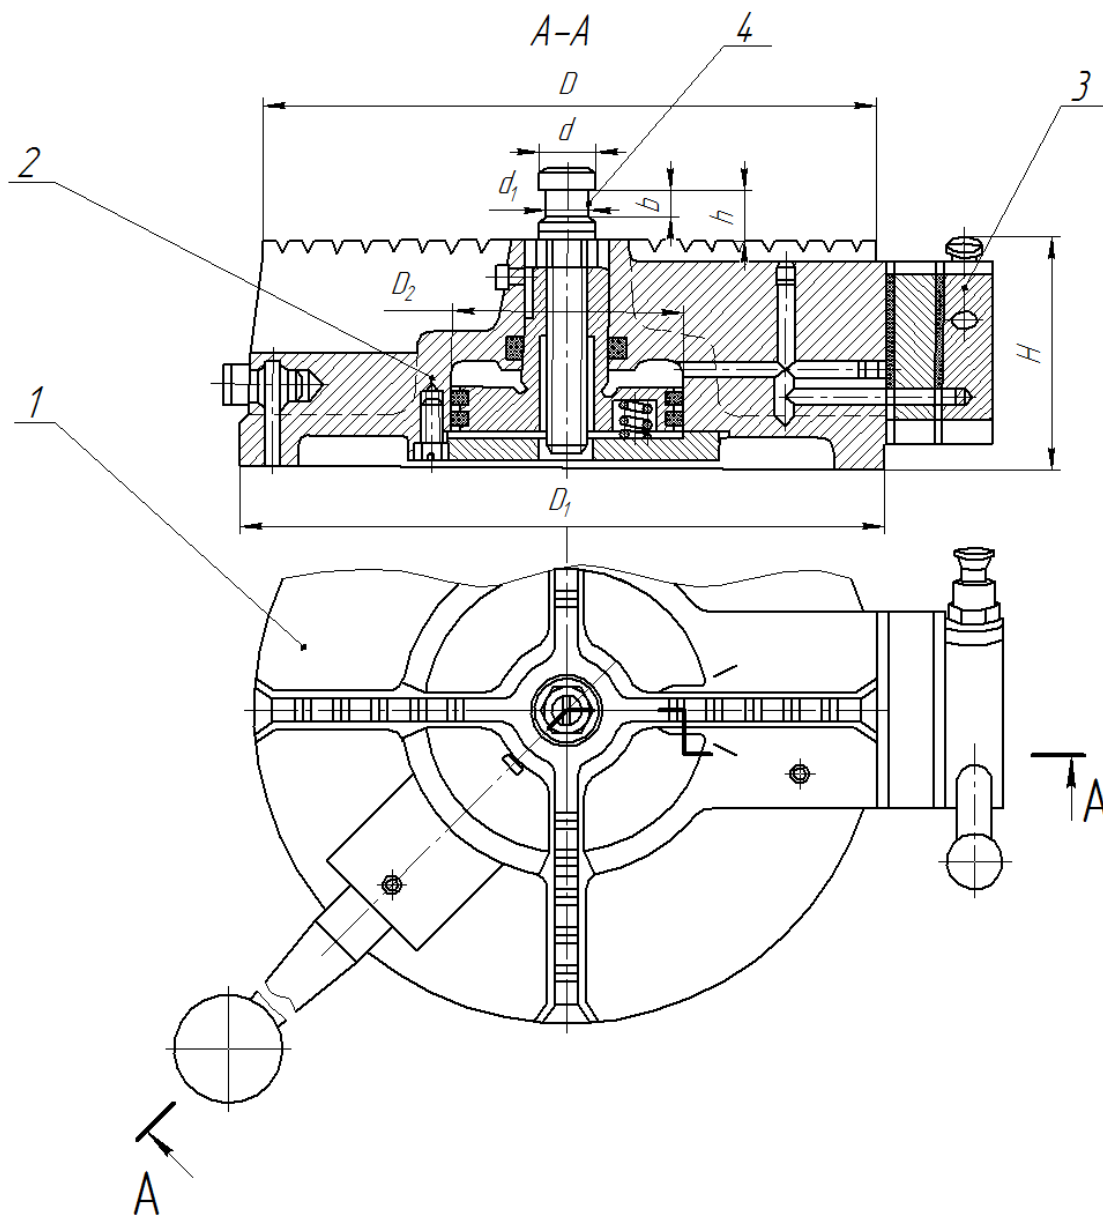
Будова й параметри підставки для накладного кондуктора із пневматичним затискачем: 1 – корпус; 2 – пневматичний циліндр; 3 – перемикач; 4 – тяга
